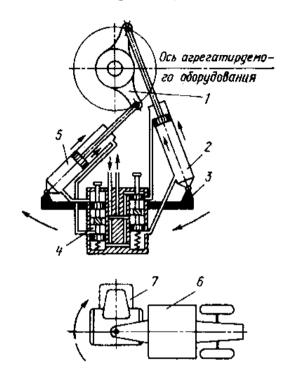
Схемы поворотного механизма и поворота агрегата: 1 – поворотный кронштейн; 2, 5 – гидроцилиндры поворота; 3 – рама тягача; 4 – гидрораспределитель; 6 – скрепер; 7 – тягач
